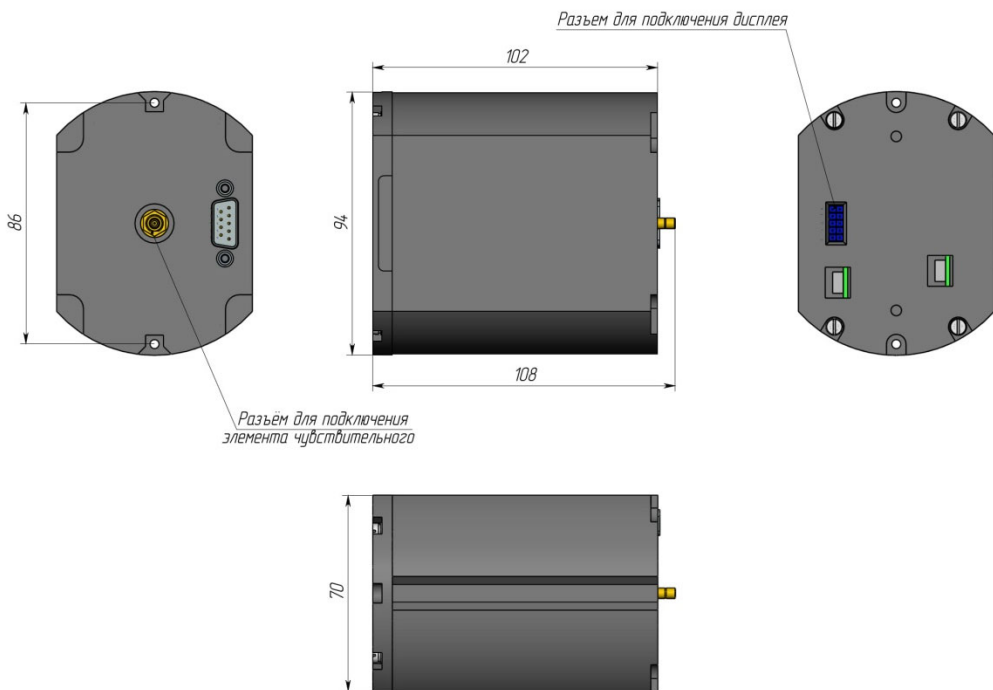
Габаритные и установочные размеры блока электронного ТЕКФЛЕКС для алюминиевых и стальных корпусов
